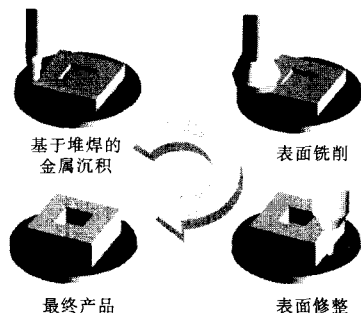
基于 GMAW 焊接与铣削的快速成形系统原理图
